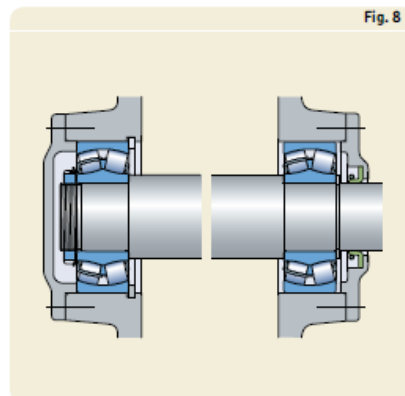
Rodamientos de rodillos a rótulas. En la imagen se puede observar una disposición de montaje fijo, libre de rodamientos de rodillos a rótulas. (SKF, 2019)
